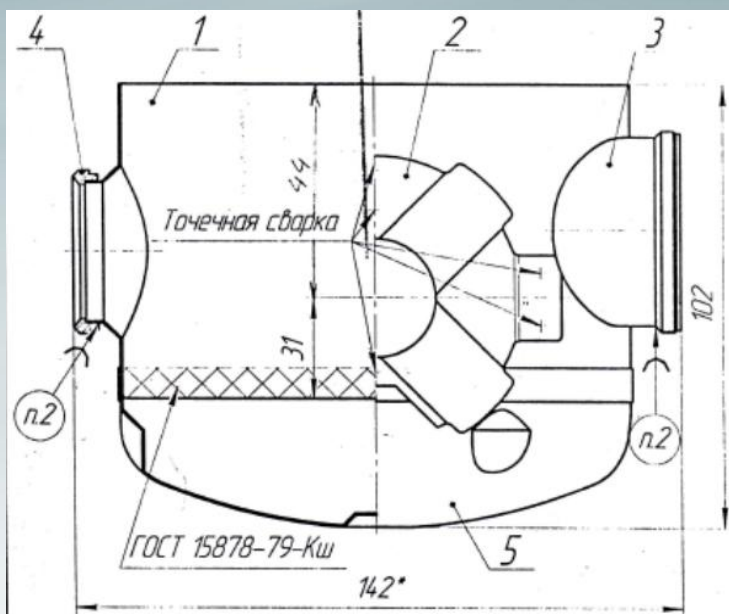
Сварные соединения детали внешний стакан холодильника
